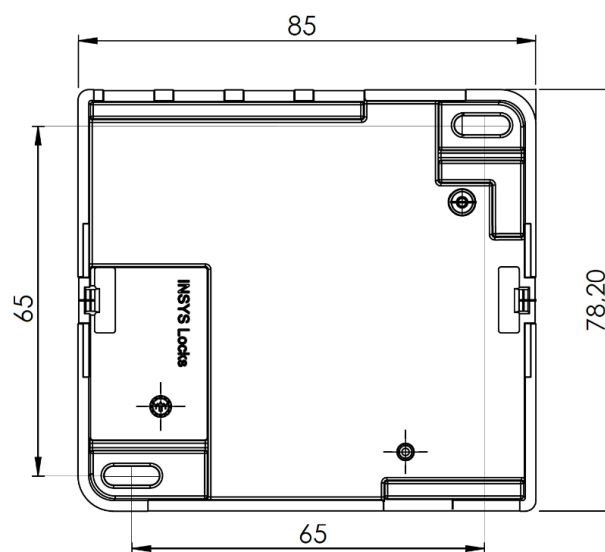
Bohrbild zur Montage von TwinIP WiFi
